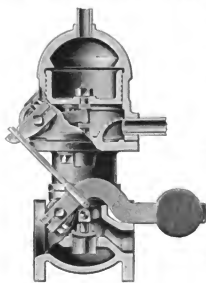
, Z. 1.: Dampfkessel-Speiseregler.
